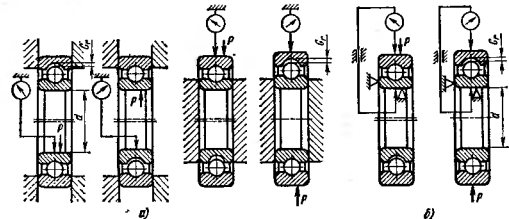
Схема измерения радиального зазора: а — с креплением колец по торцу; б — без крепления колец; G_r — радиальный зазор; P — измерительная нагрузка
